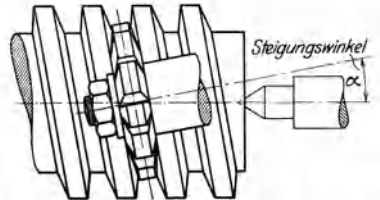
Einstellung des Fräasers für Trapezgewinde.
